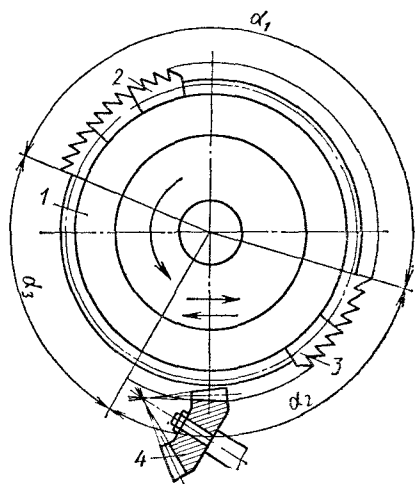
Схемы нарезания зубьев цилиндрических колес гребенчатыми фрезами
